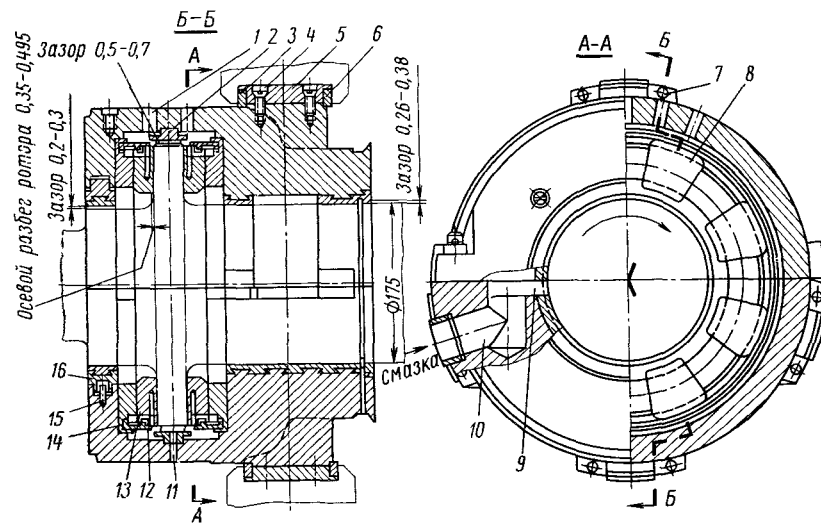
Опорно-упорный подшипник турбины ГТ-700-5 НЗЛ:
